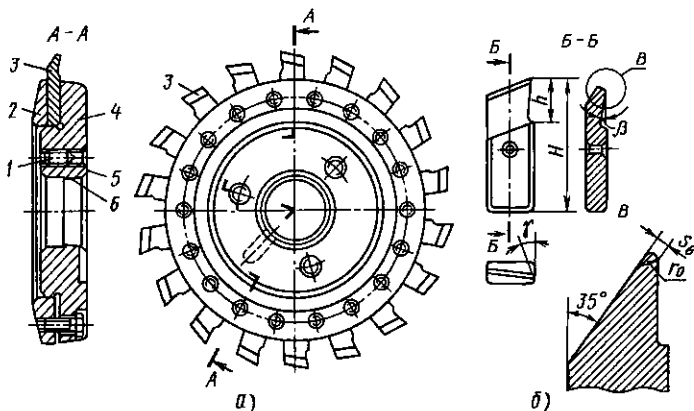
Дисковая фреза для нарезания прямозубых колес: а – общий вид фрезы; б – резец
